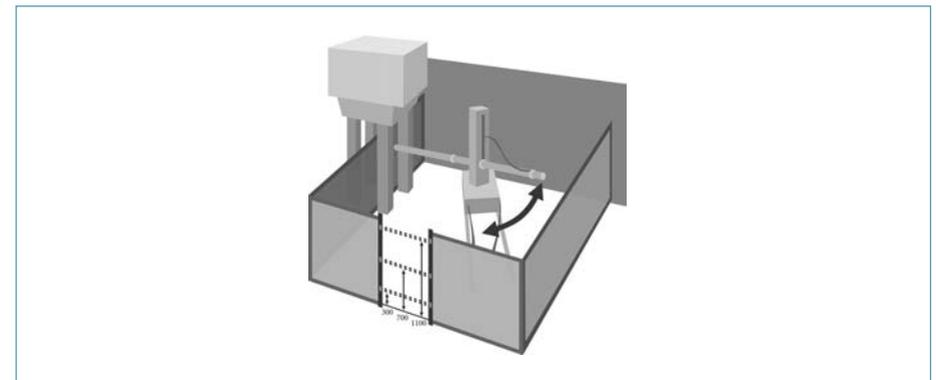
Dispositivo no separador de protección – barrera fotoeléctrica
